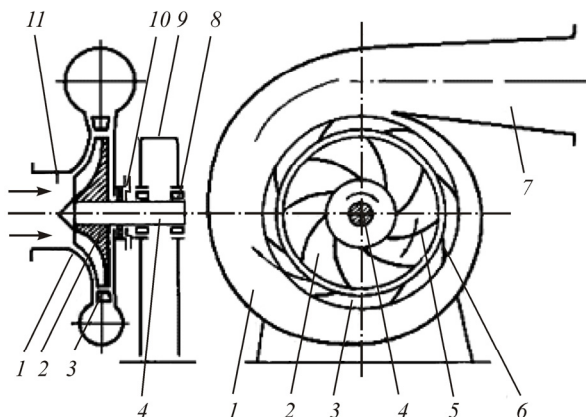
Принципиальная схема центробежного насоса: 1 – рабочая камера; 2 – рабочее колесо; 3 – направляющий аппарат; 4 – вал; 5 – лопатка рабочего колеса; 6 – лопатка направляющего аппарата; 7 – нагнетательный патрубок; 8 – подшипник; 9 – корпус насоса (опорная стойка); 10 – гидравлическое торцовое уплотнение вала (сальник); 11 – всасывающий патрубок
